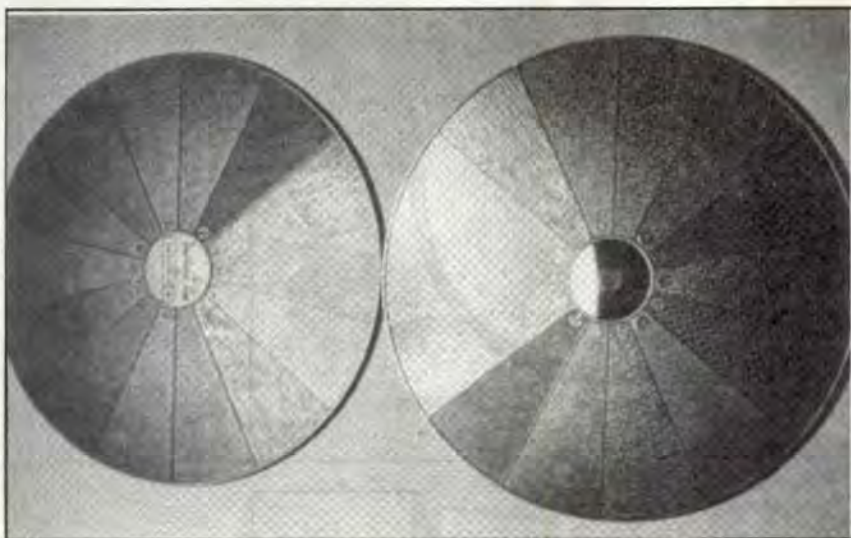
Estructuras fotografadas: a la izquierda, una placa mate de ABS, a la derecha una placa brillante de PVC
